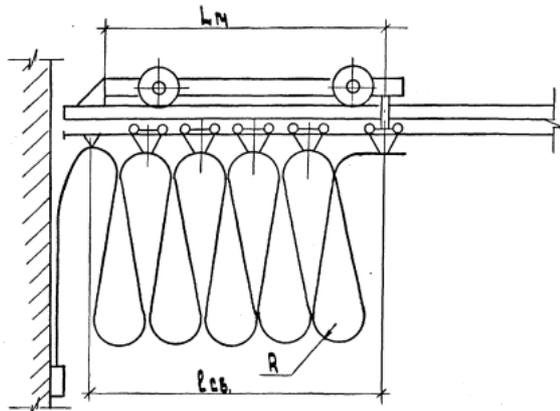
Схема свара кареток в зоне исходного положения передвижного механизма
